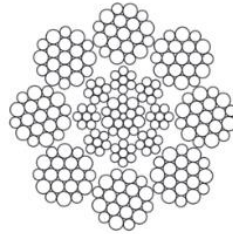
Vue de coupe du câble DRAKO 250T.
